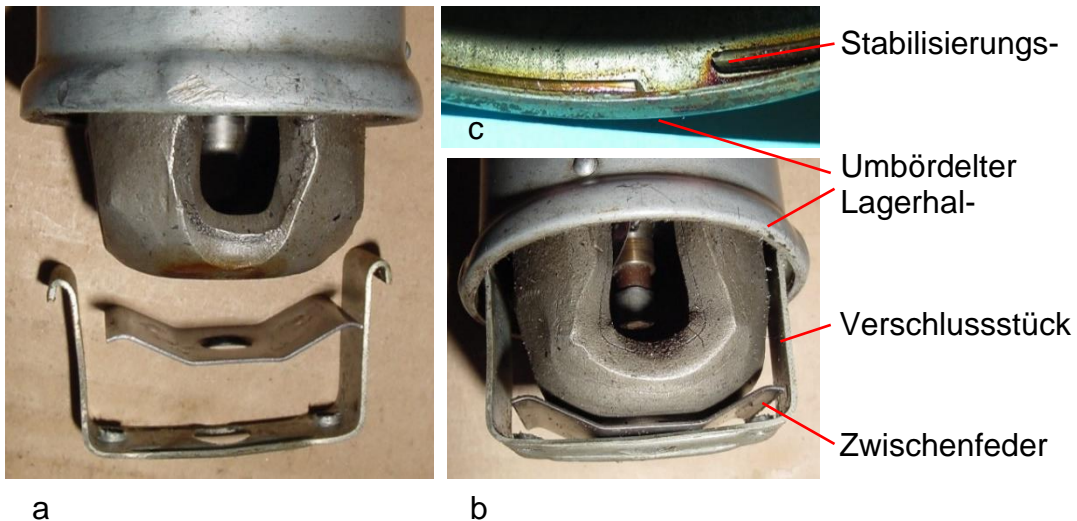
Befestigung des Magnetsystems: a) Magnetjoch, Federblech und Federklammer, b) Eingehaktes Verschlussstück, c) Stabilisierungsring
